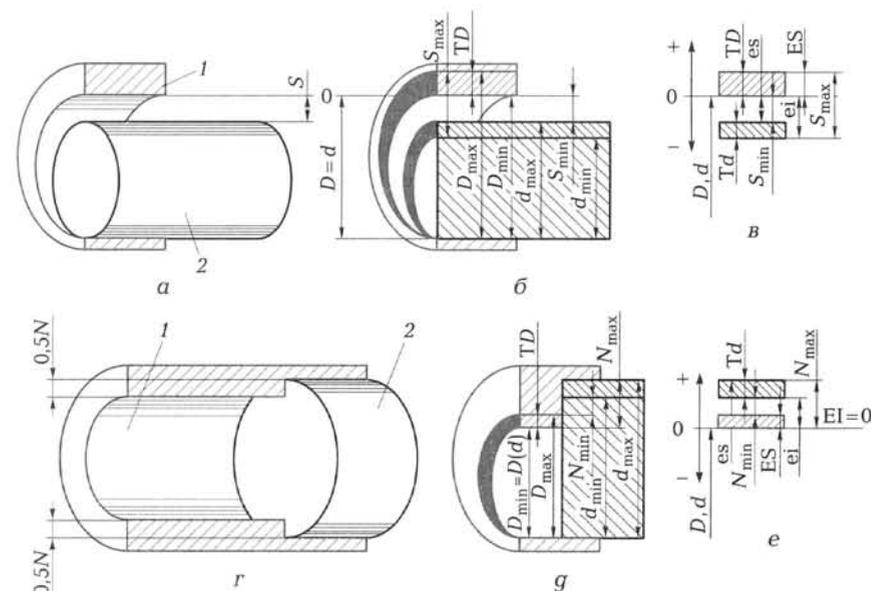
Соединение отверстия с валом и схемы расположения их полей допусков при посадках: с зазором (а...в) и с натягом (г...е):
